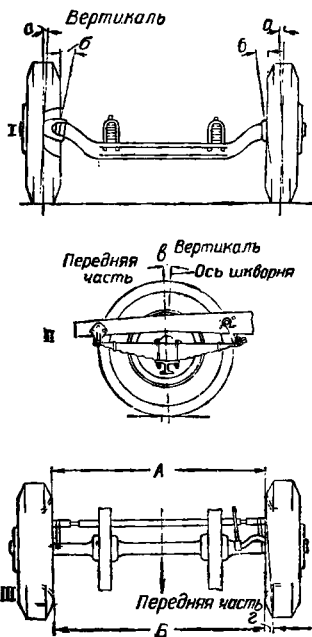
Схемы развала и схождения колес и наклона шкворней поворотных цапф.
